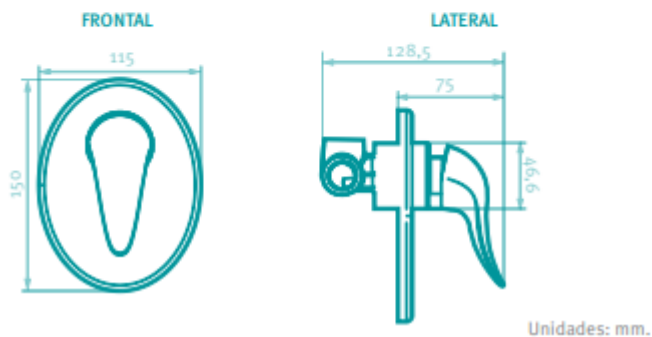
Plano Técnico ducha de bajo flujo con accesorios.
